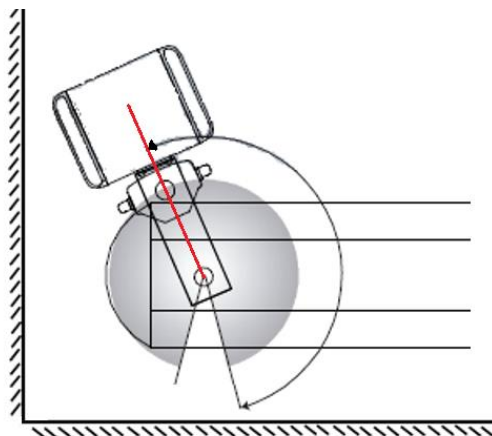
Befestigung des Drehanschlags links an einer Säule mit Auslegerarm.
